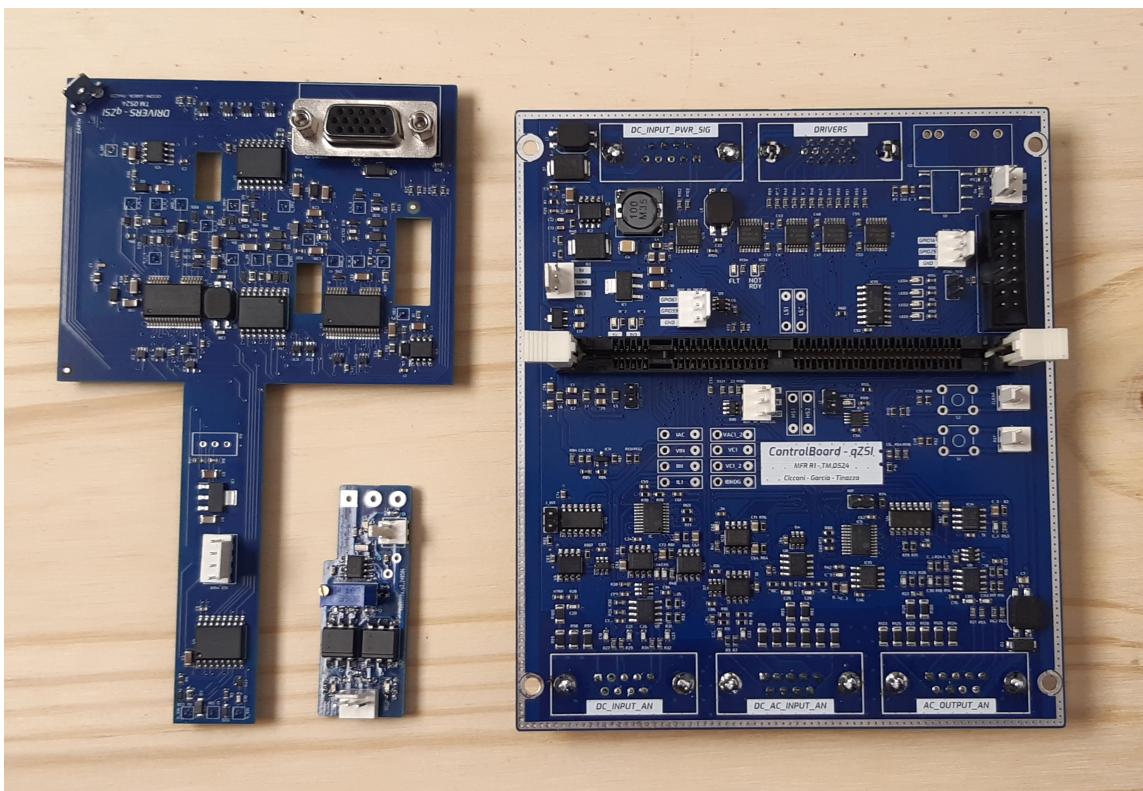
Placas fabricadas. A la izquierda: placa de drivers, en el centro: placa para controlar el transistor de entrada, a la derecha: placa de control.
